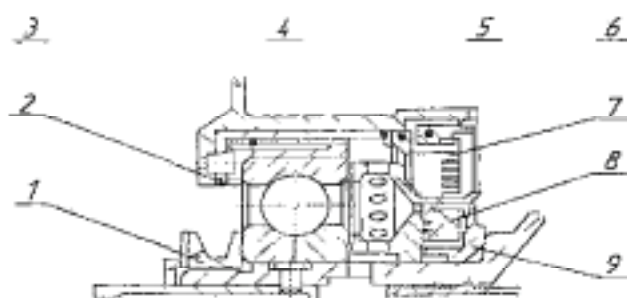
Конструкция РУП ротора ВД: 1-гайки; 2-стакан; 3-гладкое кольцо; 4-упругое кольцо; 5-втулка уплотнения; 7-втулка; 8-графитовое кольцо; 9-распорная втулка
